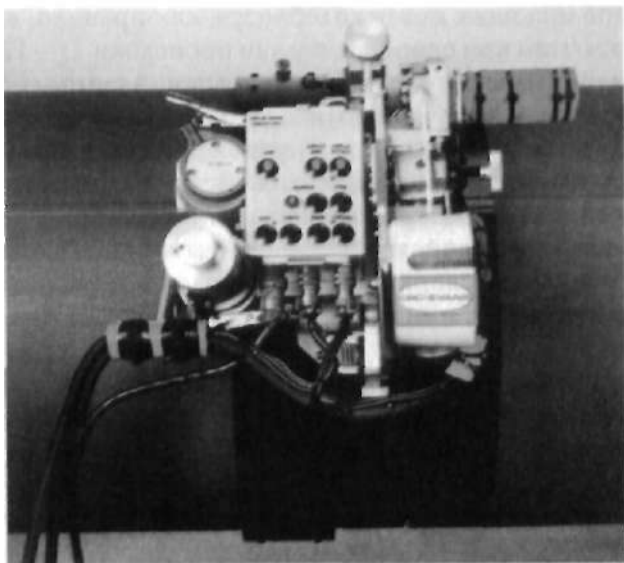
60. Наружный сварочный аппарат CRC-Evans (внешний вид):
